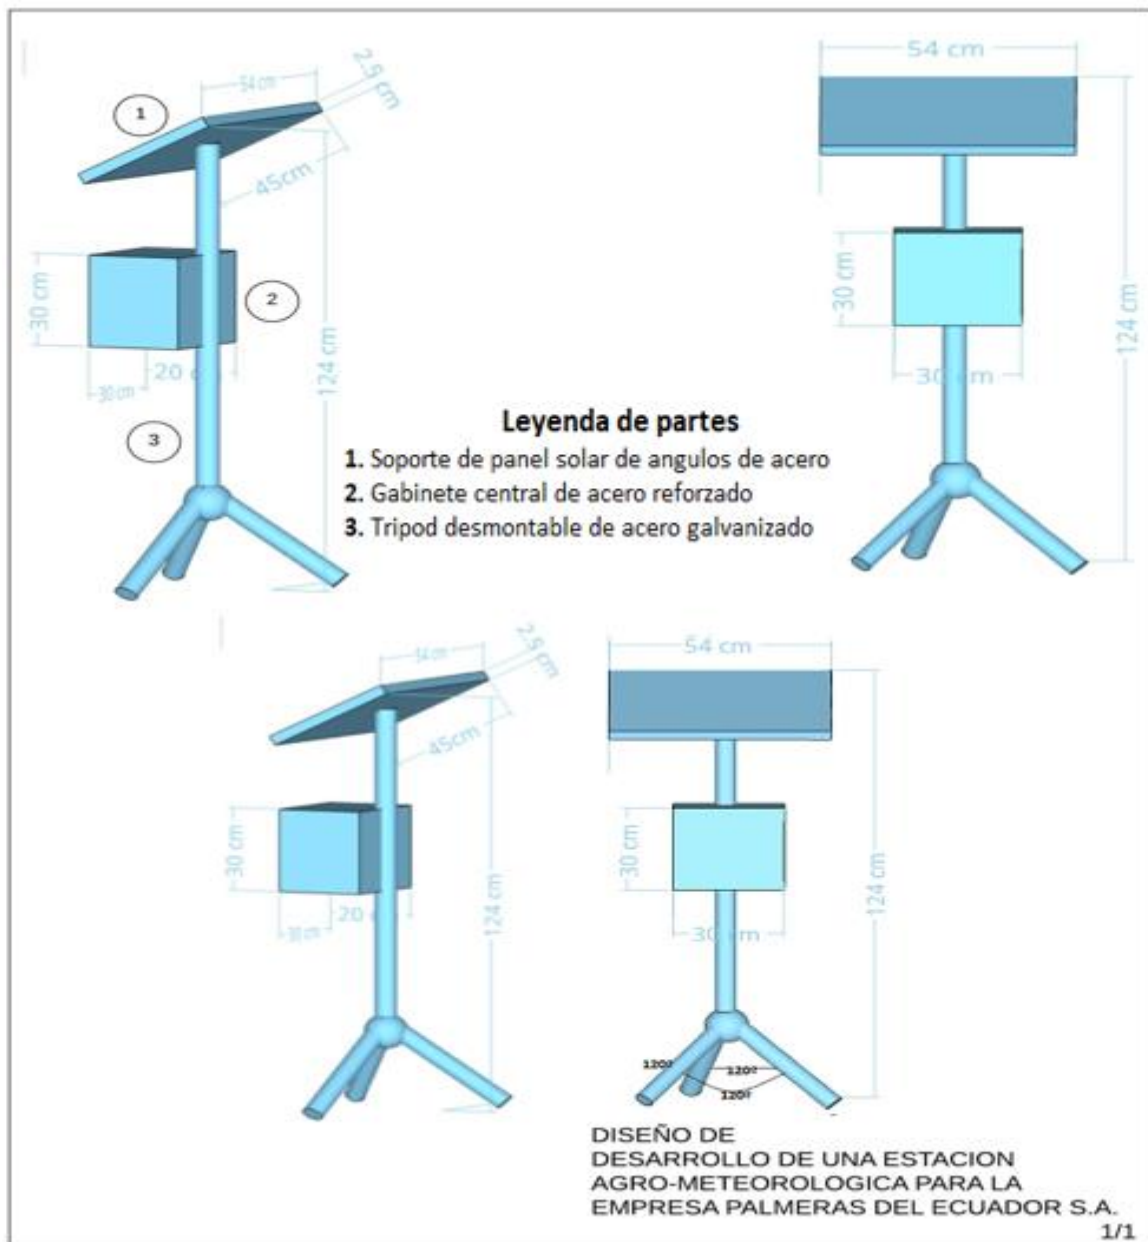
7. Dimensiones del diseño mecánico de la estación, Fuente: Elaborado por el autor
